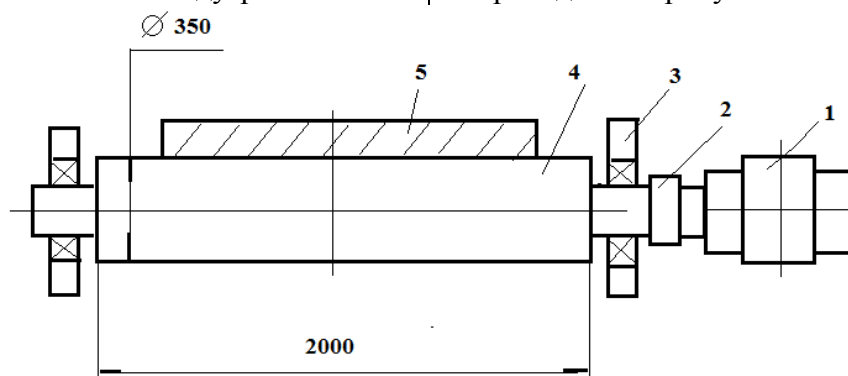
Схема привода ролика рольгага РПМ: 1- электродвигатель, 2- муфта, 3- подшипниковые опоры, 4- бочка ролика, 5 - лист
